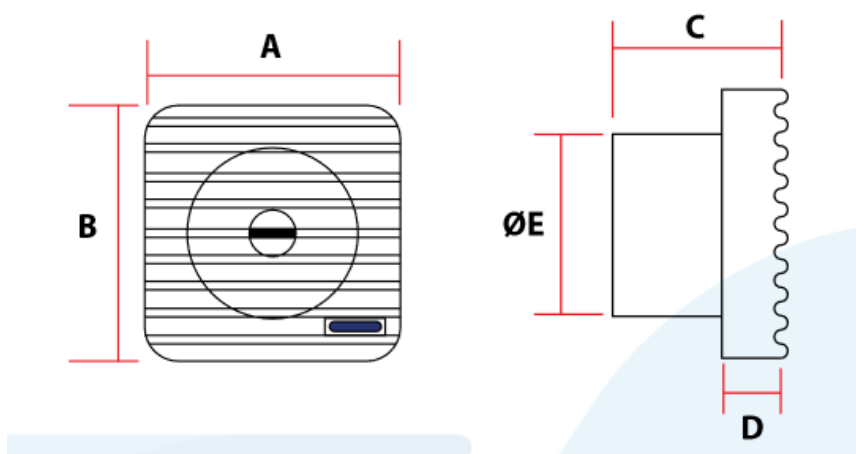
Exaustor modelo MultiVac – Muro 150B - 220V.
